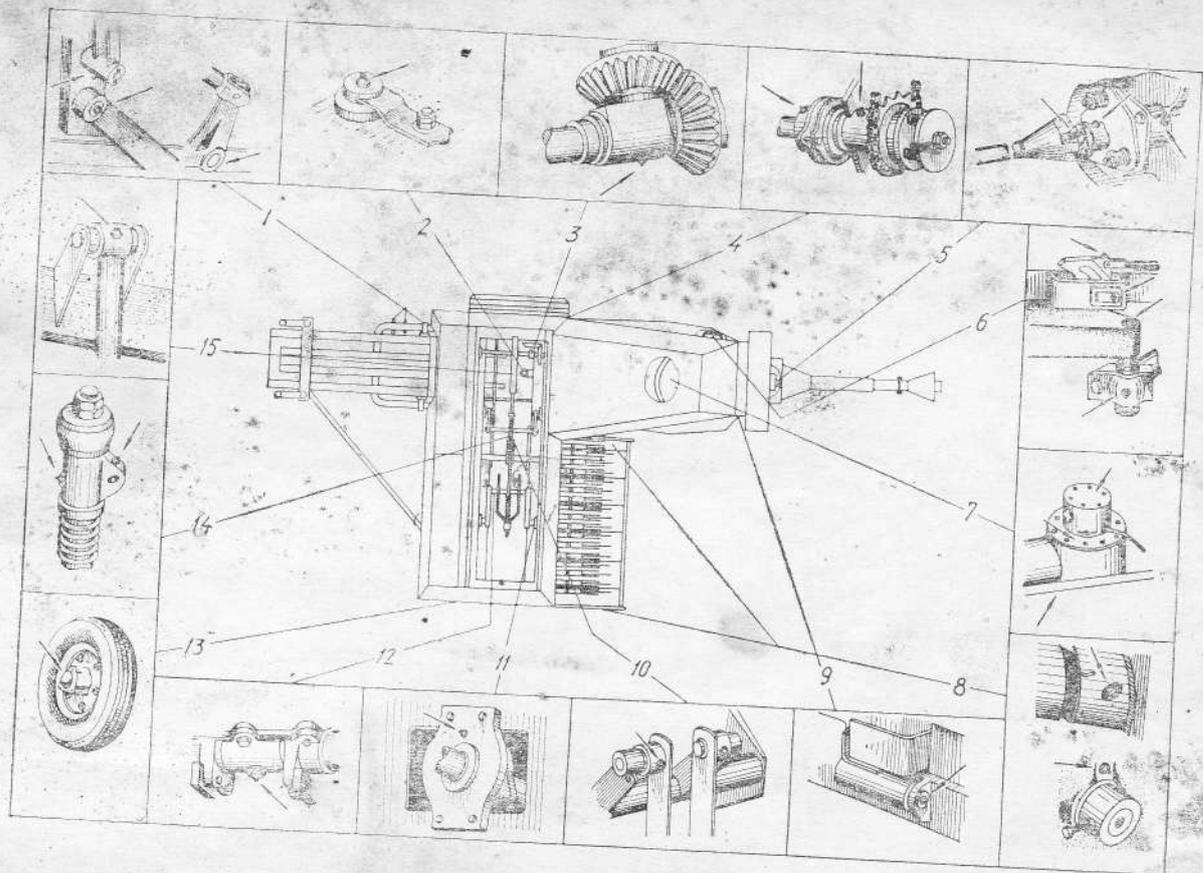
Схема смазки пресс-подборщика (см. таблицу смазки)
